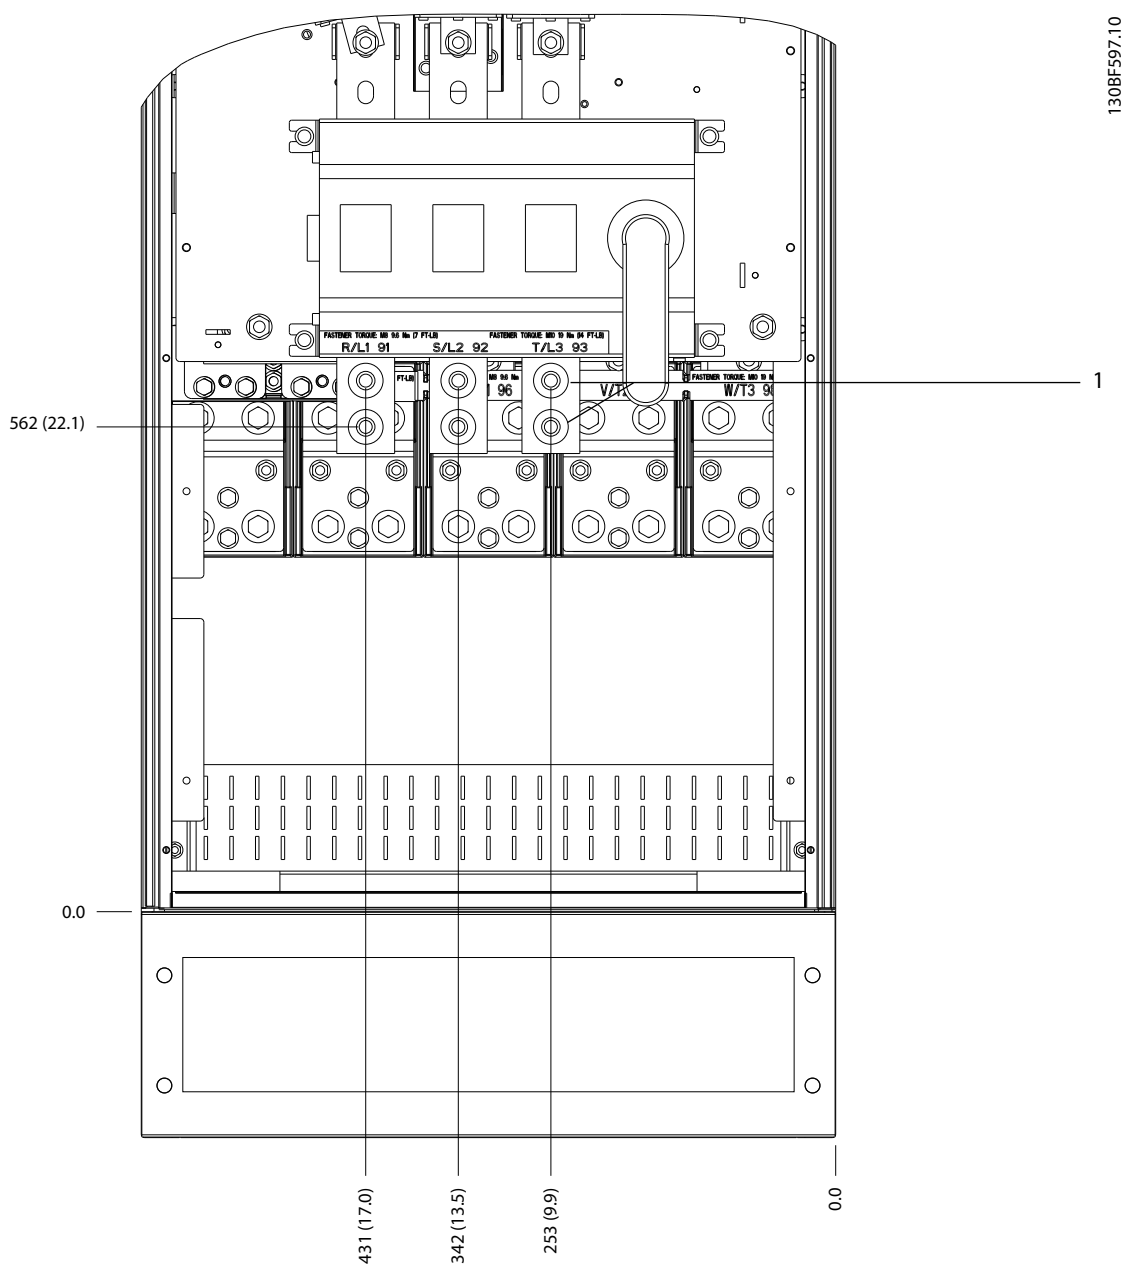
Klemafmetingen voor E1, vooraanzicht
